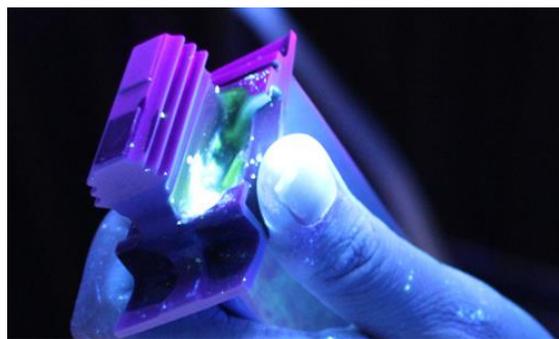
Ejemplo de inspección por líquidos penetrantes
